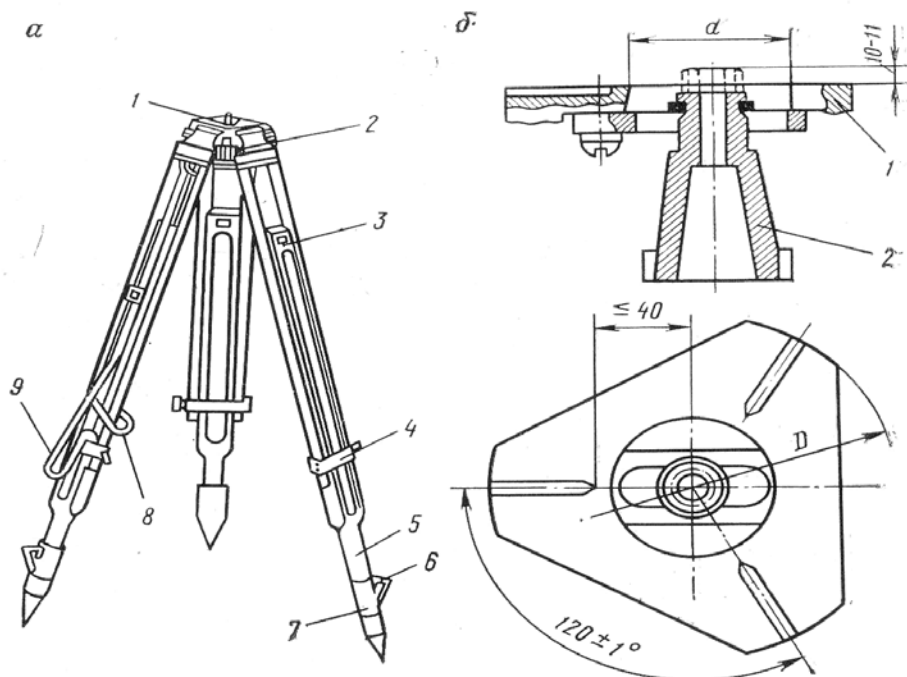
Раздвижной штатив для геодезических приборов: а – общий вид; б – головка штатива; 1 – головка; 2 – становой винт; 3 – ограничитель; 4 – зажимное устройство; 5 – ножка; 6 – упор; 7 – наконечник; 8 – стягивающий ремень; 9 – плечевой ремень
